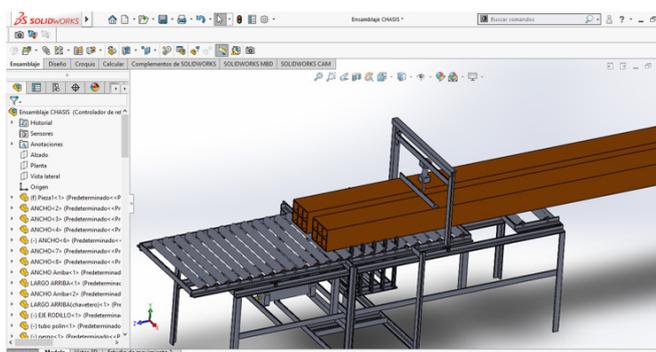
Diseño en CAD del equipo desarrollado en este trabajo.
